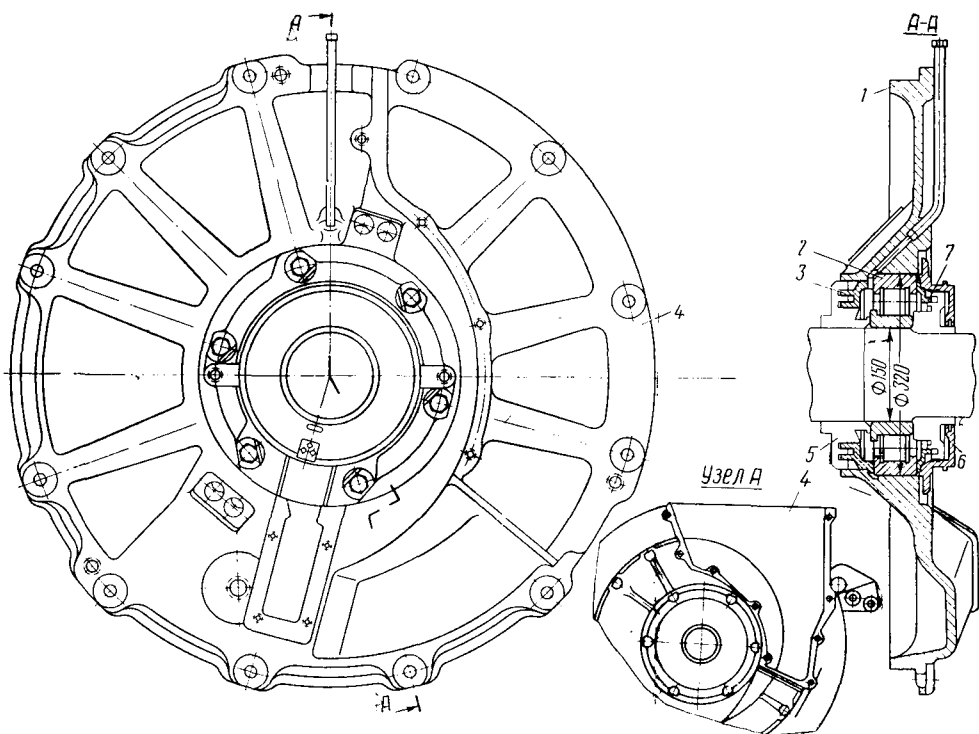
Щит подшипниковый двигателя НБ-418К6
